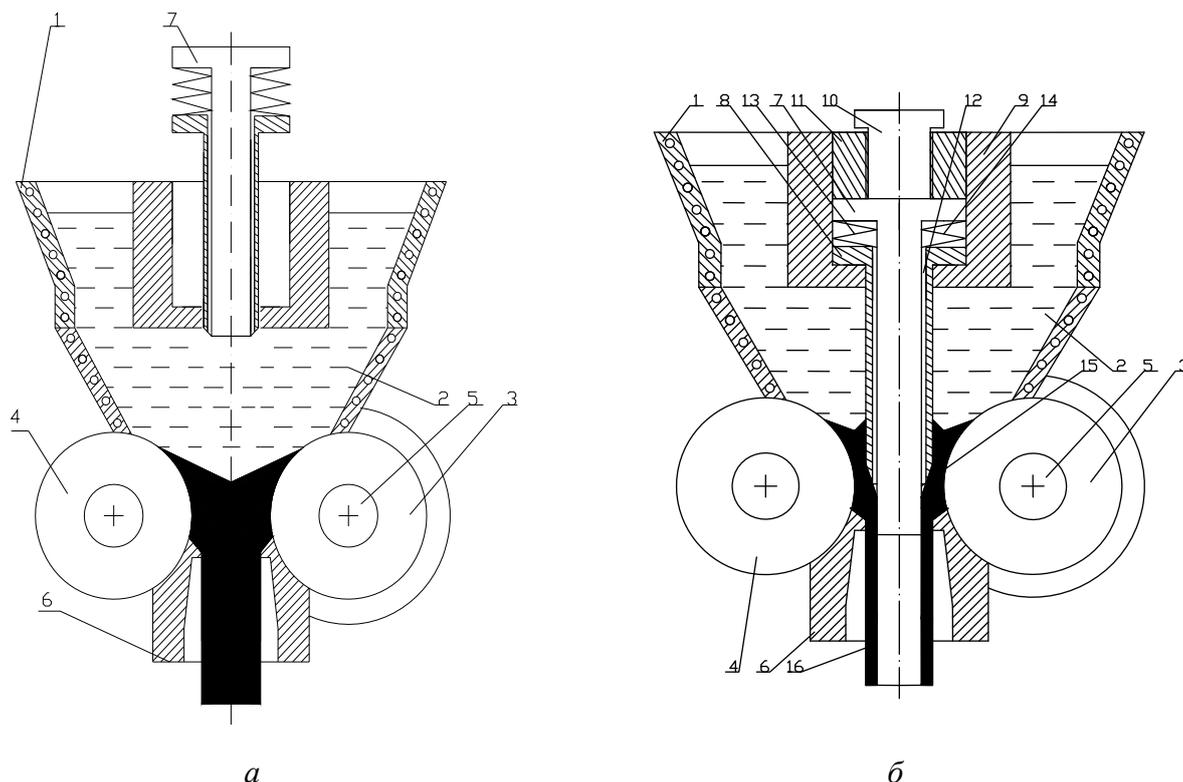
Устройство для беслитковой прокатки-прессования сплошных (а) и полых (б) пресс-изделий
